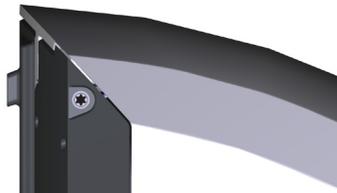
Position der Torx T25-Schrauben zum Lösen, Einstellen und Befestigen des Gehäuses
